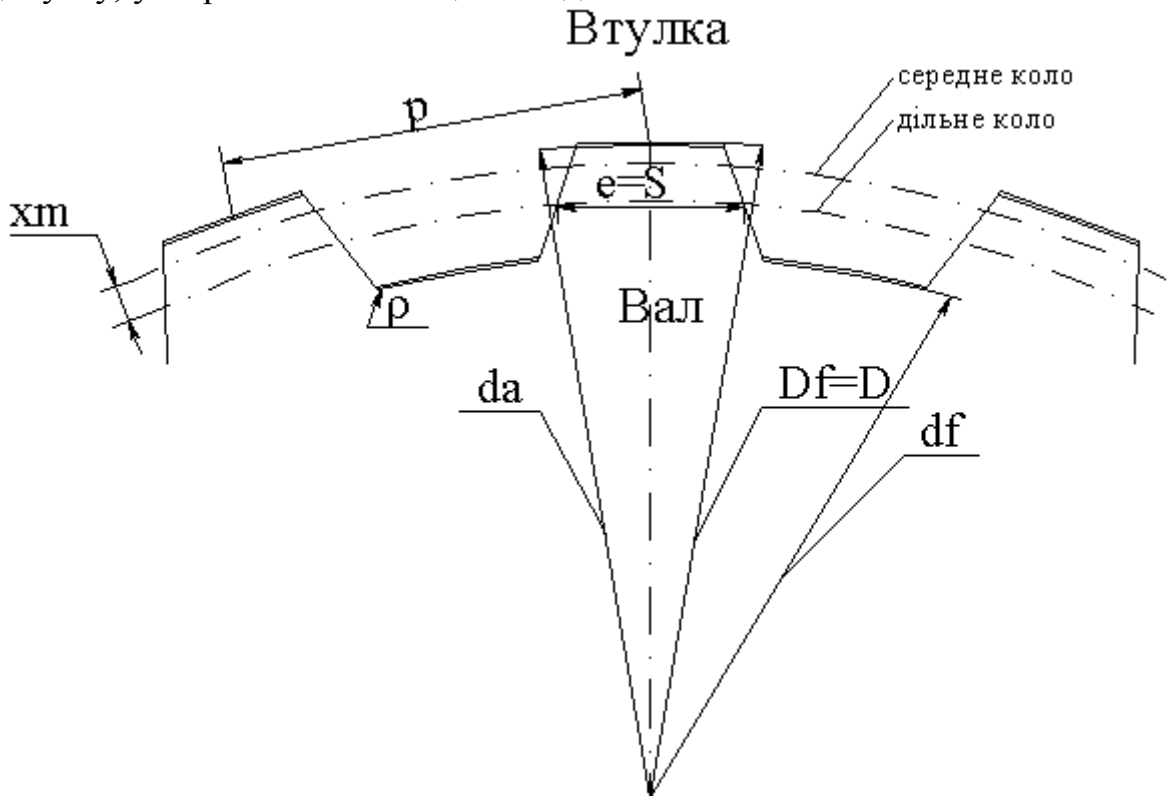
Центрування за бічними поверхнями зубців
